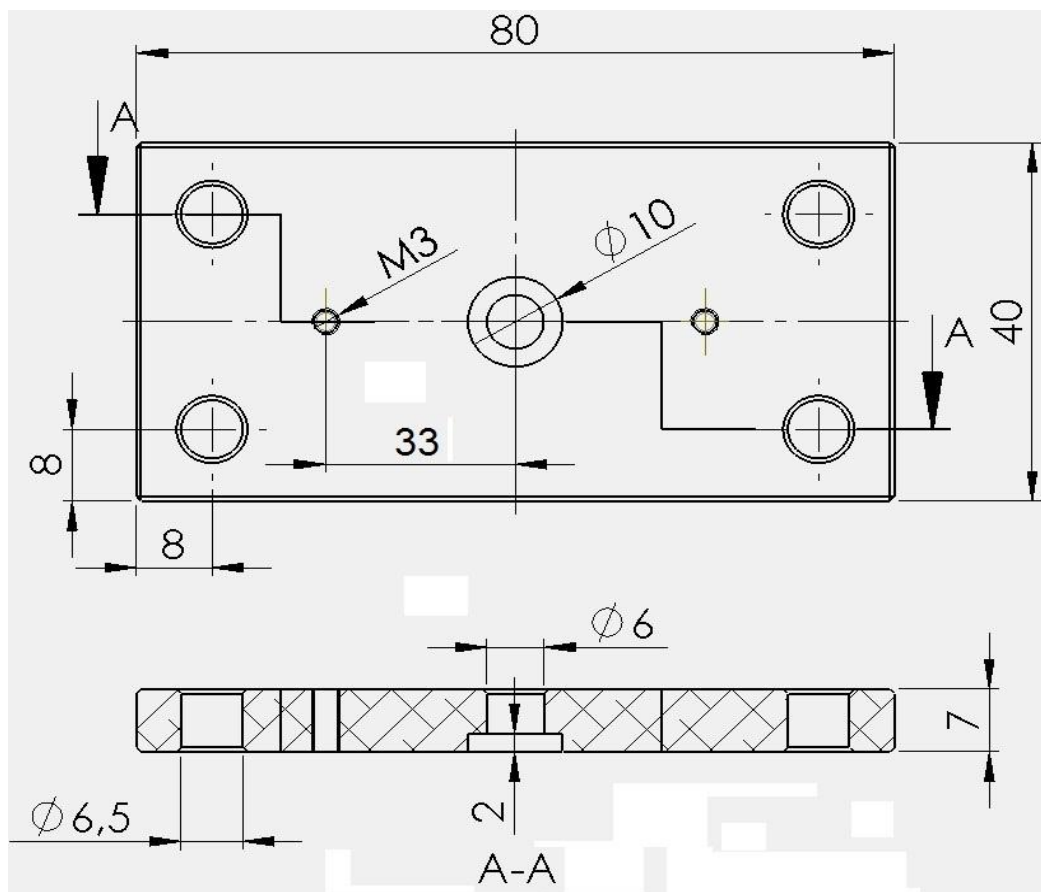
Desenho técnico da placa de suporte ao motor de passo.
